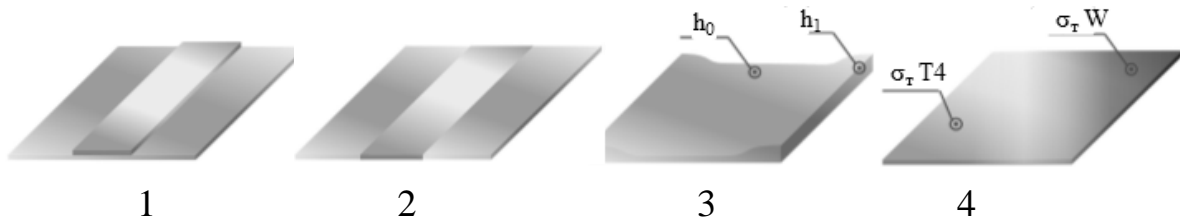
Класифікація штаб з різними механічними властивостями за способом виробництва: 1 - Patchwork Blanks; 2 - Tailor Welded Blank; 3 - Tailor Rolled Blanks; 4 - Tailor Heat Treated Blanks [1]
